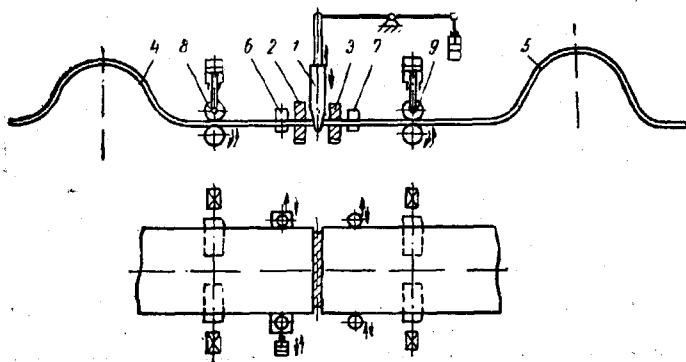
Схема машины МСЛ-200-2 с гратоснимающим устройством для стыковой сварки полос.
